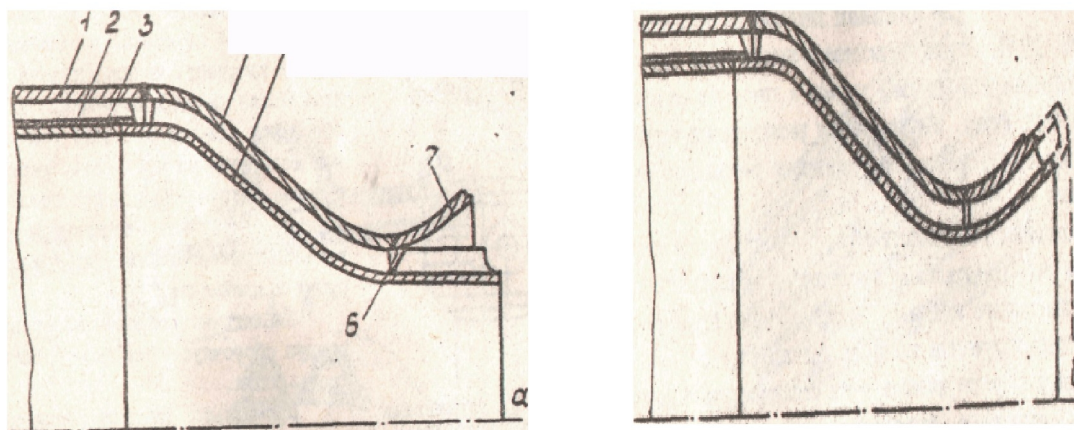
Положение деталей рубашки и стенки средней части корпуса камеры до (а) и после (б) развальцовки цилиндрического участка стенки: 1, 2, 3- рубашка, гофрированная проставка и стенка цилиндрического участка корпуса, 4, 5 - рубашка и стенка входной части сопла, 6 - кольцевая проточка в ребрах, 7 - рубашка начального участка расширяющейся части сопла
